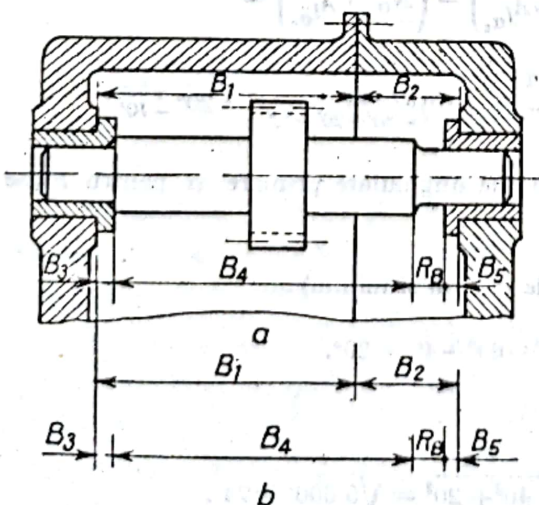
Lanț de dimensiuni din ansamblu unui reductor.
